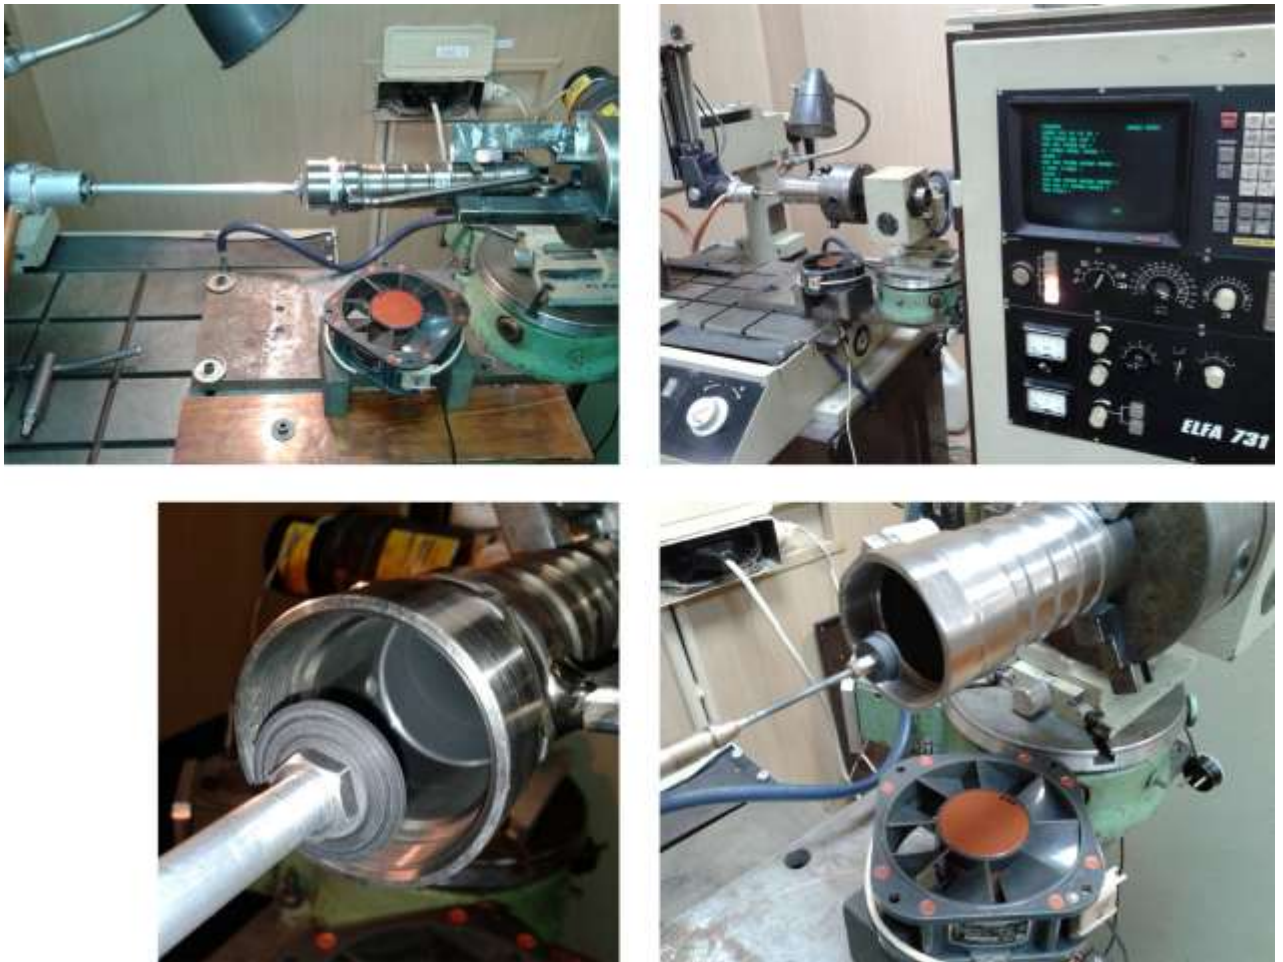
Установка ELFA731 для нанесения покрытий во время ЛКО цилиндров различных типоразмеров
